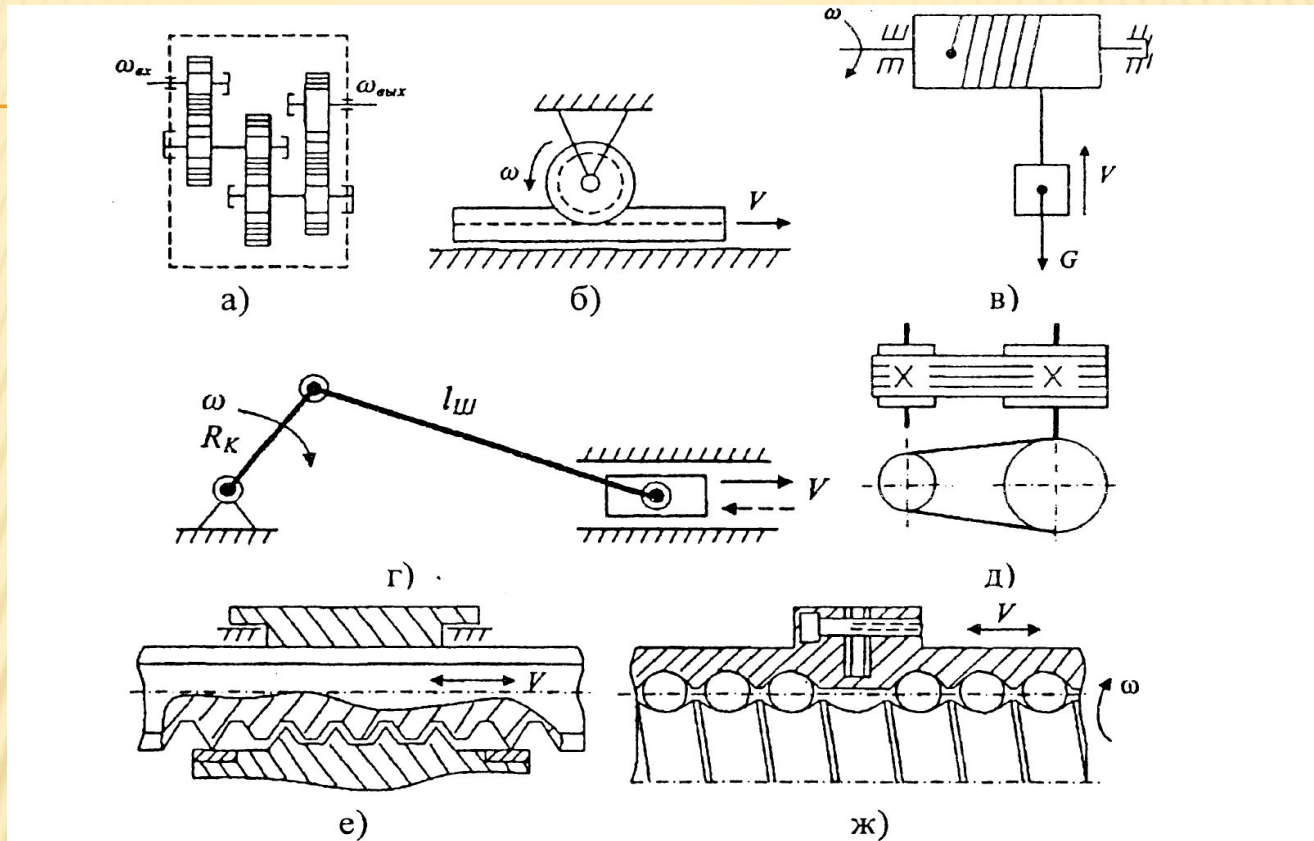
1. Механические передаточные устройства: а — редуктор; б — зубчато-реечная передача; в - барабанно-канатная передача; г — кривошипно-шатунный механизм; д — ременная передача; е — винтовая передача; ж — шарико-винтовая передача
